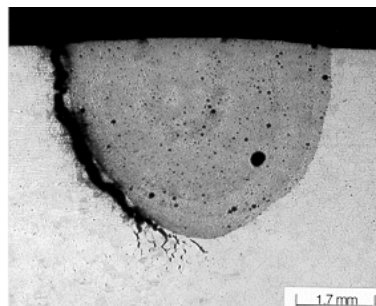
Fractura en el pie de la soldadura de la soldadura (28)
